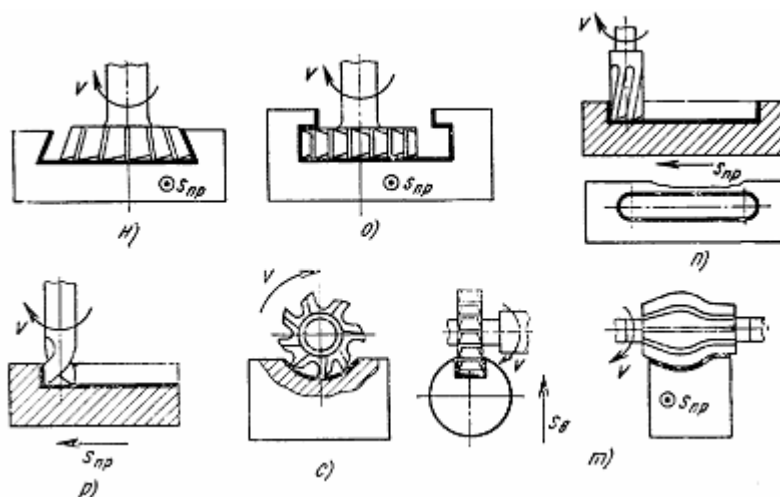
Обработка заготовок на горизонтально- и вертикально-фрезерных станках
